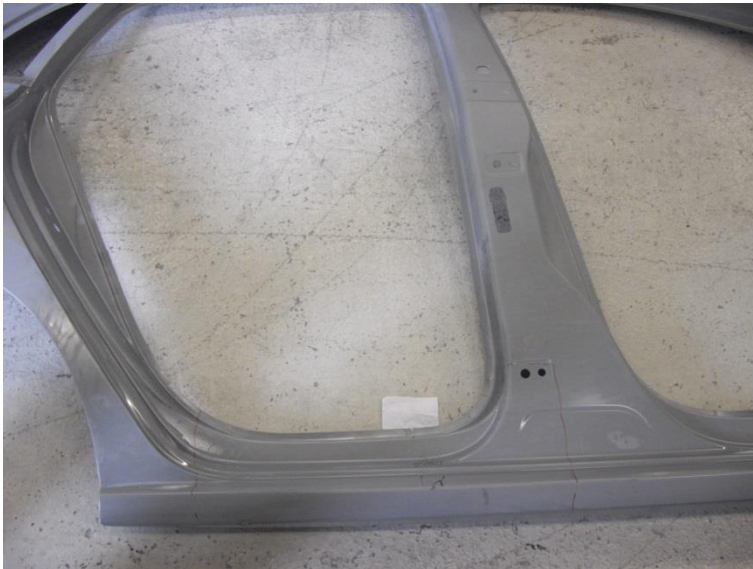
Foto lateral derecho 4 puertas con grieta
